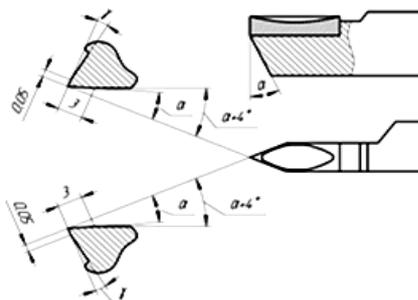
Резьбовой резец со сменной твердосплавной пластиной
